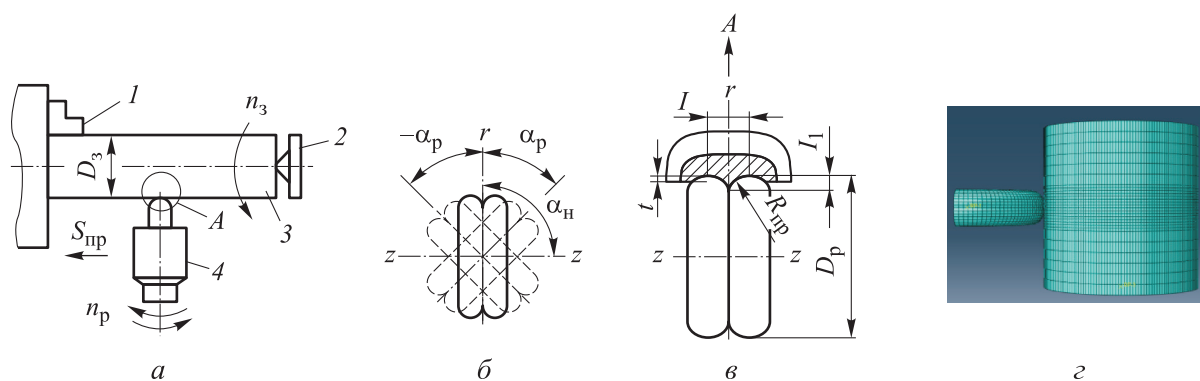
Реверсивное выглаживание поверхности заготовки роликом:
